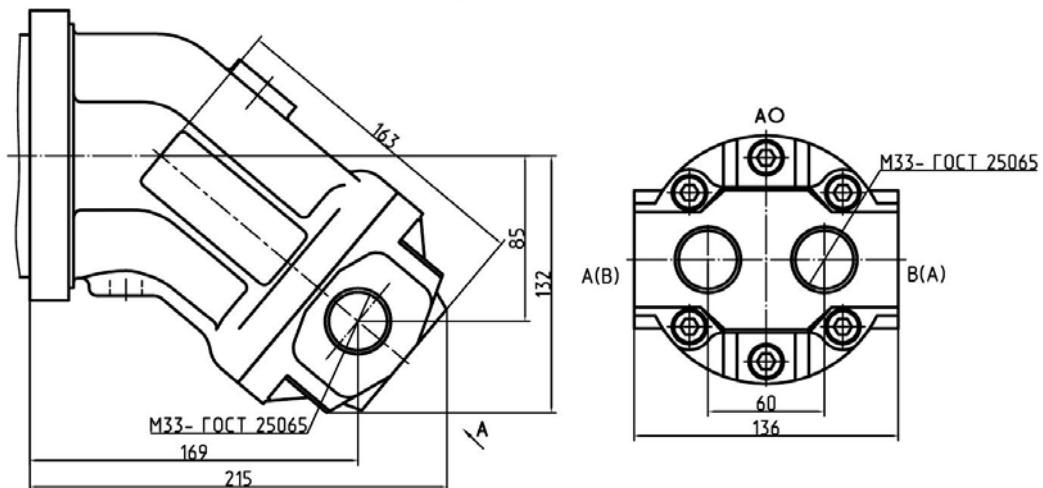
Габаритные, присоединительные размеры в гидромоторах 410.0.45(56;63).
